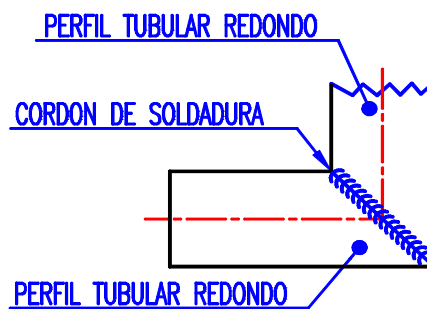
(b) Esquema de la soldadura PLACA-EJE
